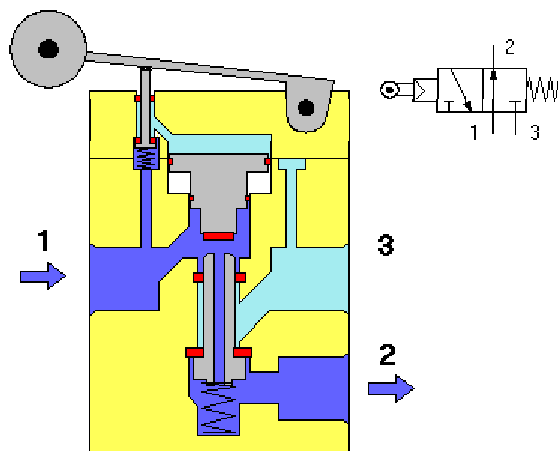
Válvula 3/2 inicialmente abierta accionada por rodillo
